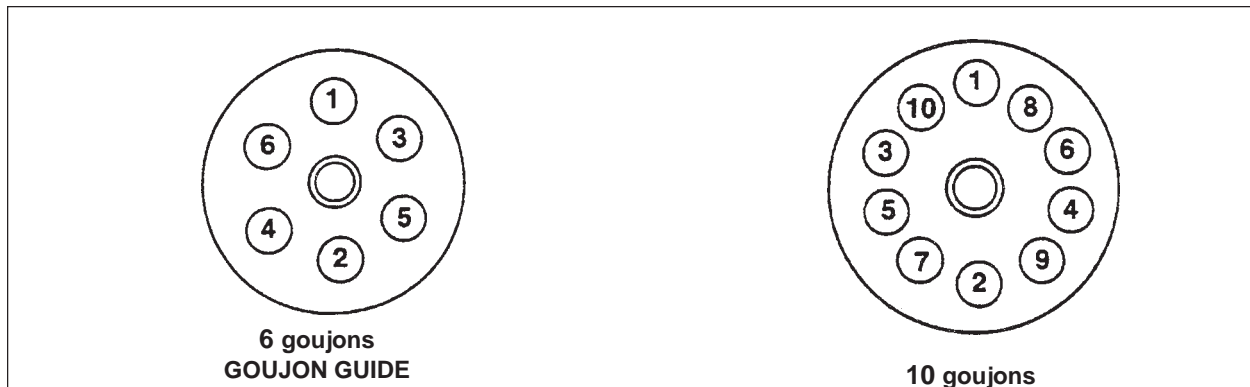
SÉQUENCE DE SERRAGE DES ÉCROUS
